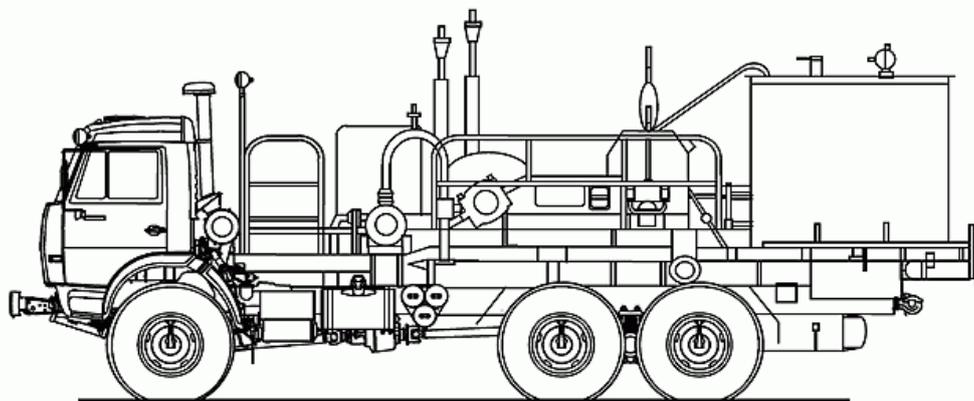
Общий вид цементировочного насосного агрегата СИН-35.05
